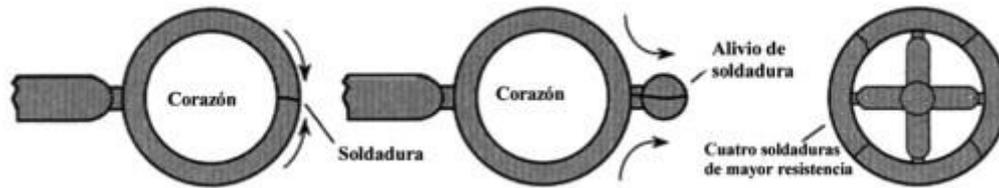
Método para evitar las líneas de soldadura mediante alivios.
